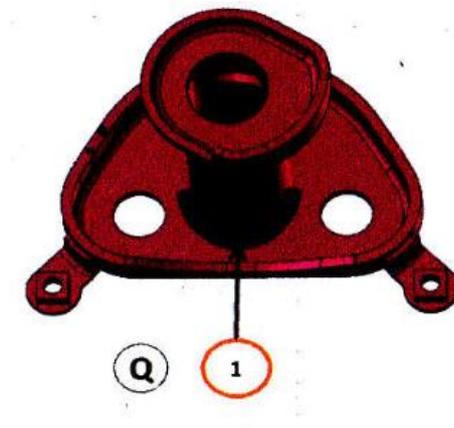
Titik Pengelasan Welding 1
